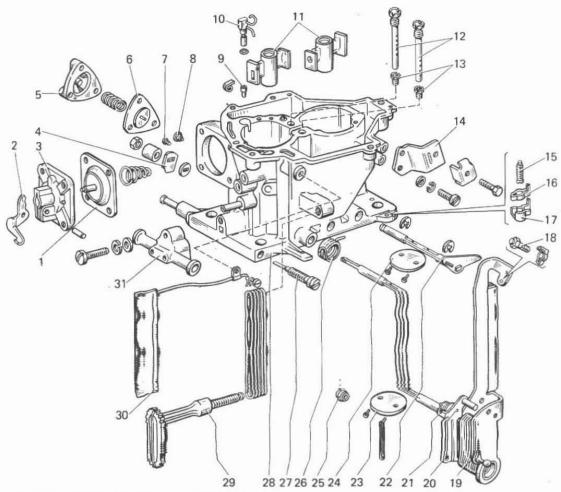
Piezas del cuerpo del carburador 21053-1107010:
